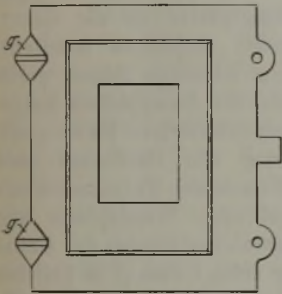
Ansicht einer Gelenk-Modellplatte.
